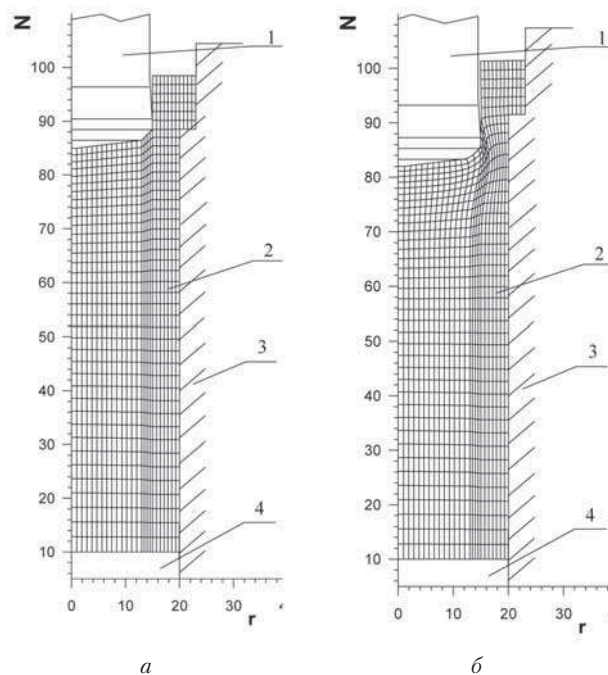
Вихідна (а) та zdeформована (б) заготовки (розміри в міліметрах: 1 – пуансон, 2 – заготовка, 3 – матриця, 4 – виштовхувач)
